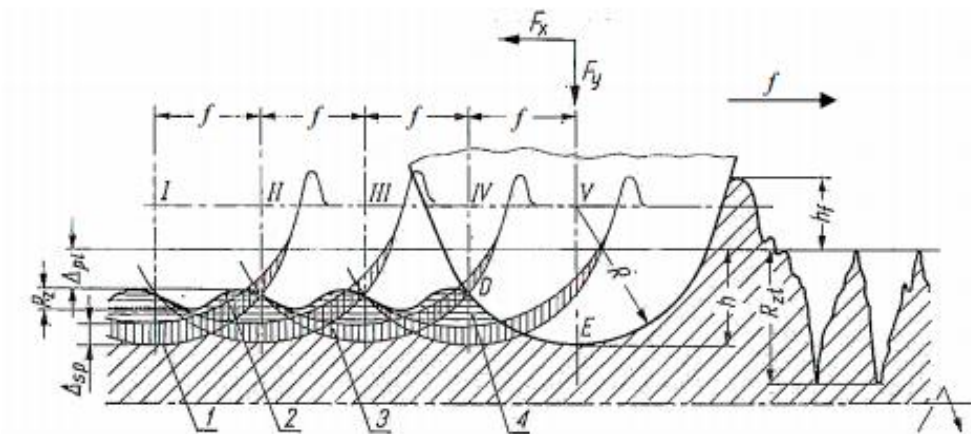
Механізм формування поверхні при обкочуванні кульками [26]
